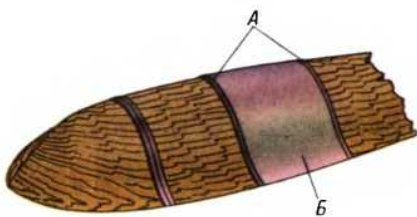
Опайка корпуса листами жести: А — тавровый шпангоут; Б — лист обшивки.
